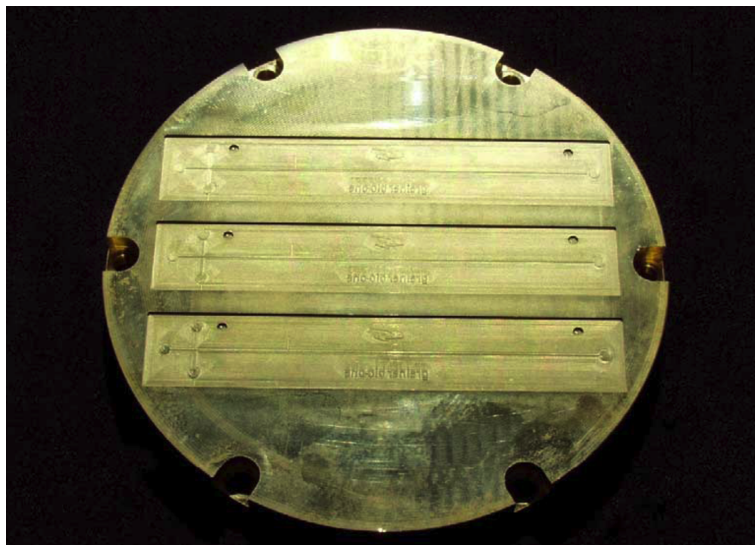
Bild des Messingprägwerkzeugs.
